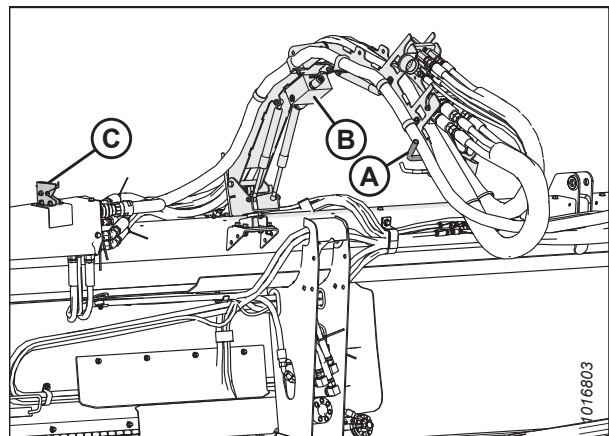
Styringssystem til hydraulikslange – alle skærebørde undtagen D215
